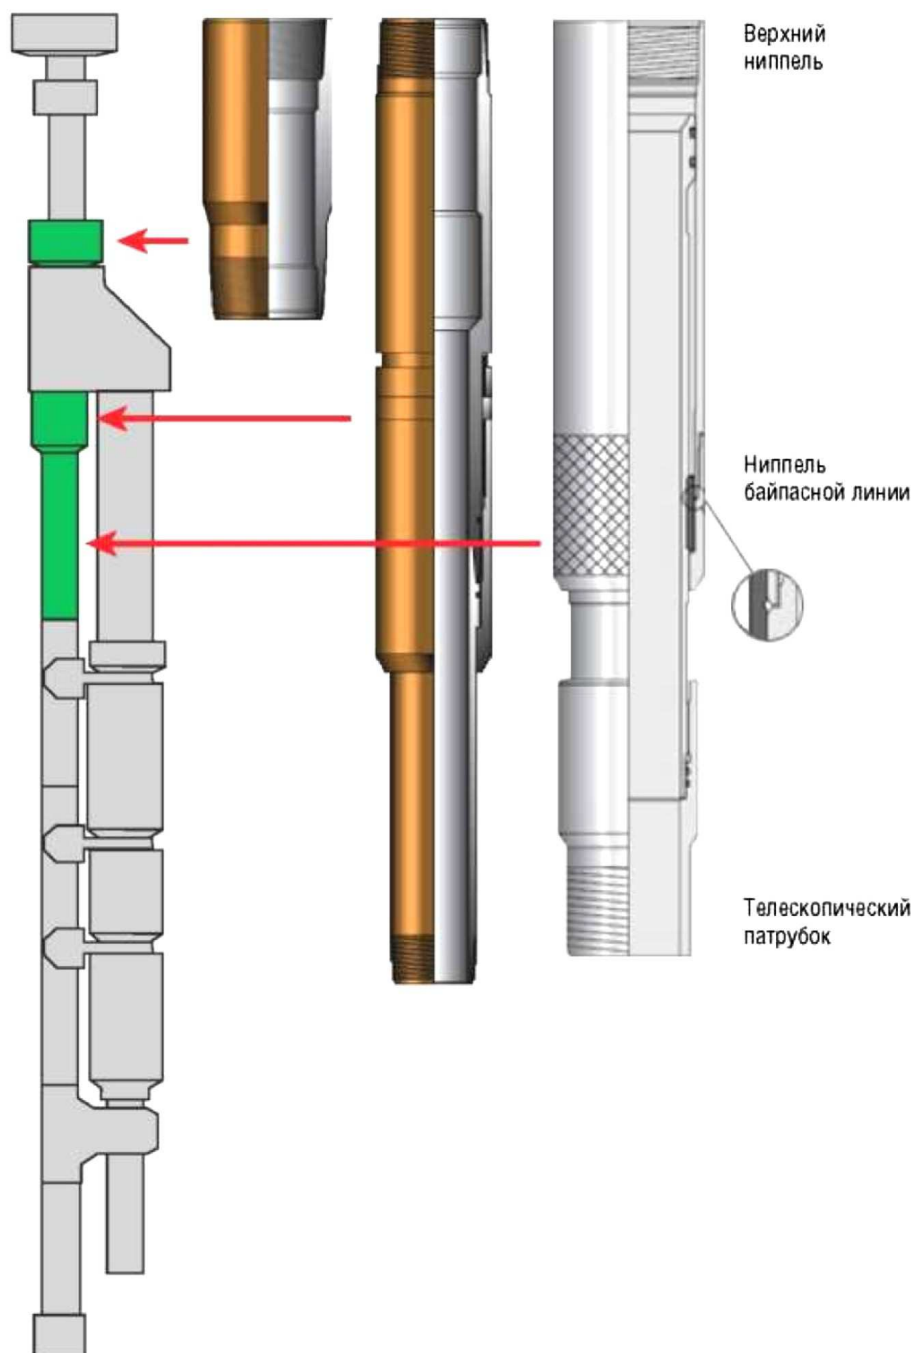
Верхний ниппель, ниппель байпасной линии и телескопический патрубок
